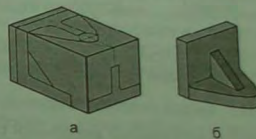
Общий вид размеченной заготовки (а) и модели отливки, выточенной из заготовки (б)
